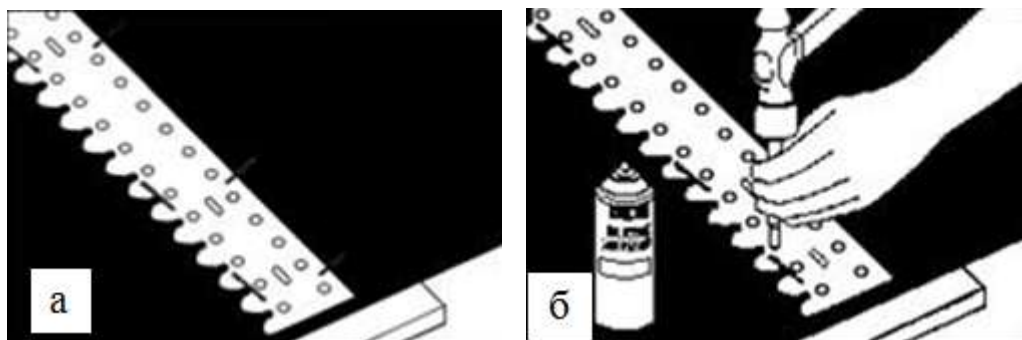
Установка шаблона и подготовка отверстий в ленте
